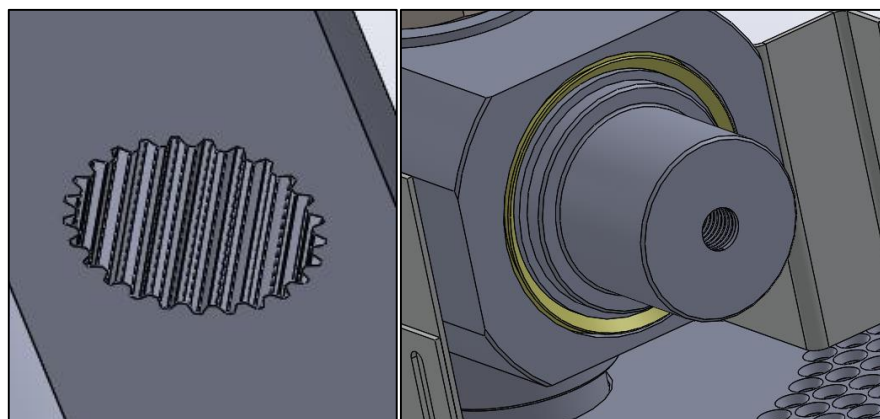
Imagen izq.: Perforación pasante estriada. Imagen der.: Sello anillo V montado sobre una cavidad del eje de rodillos.
